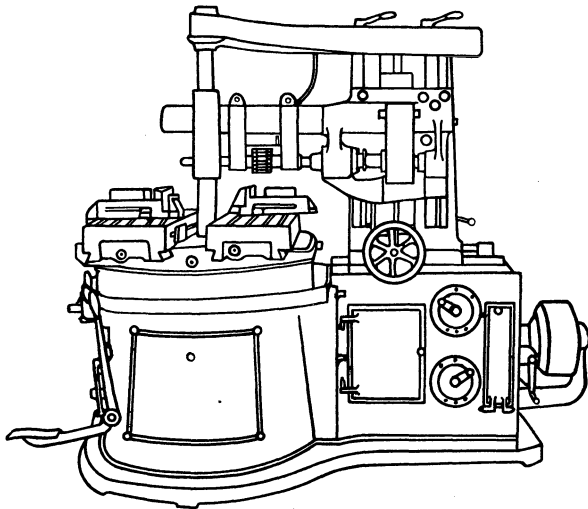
Fräsmaschine mit zwei Aufspanntischen von Potter & Johnston.
